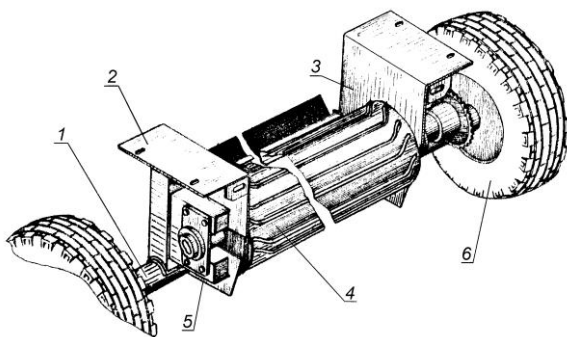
Основание камеры: 1 – ось, 2 и 3 – боковины; 4 – валец нижний задний; 5 – корпус подшипника; 6 – колесо.
